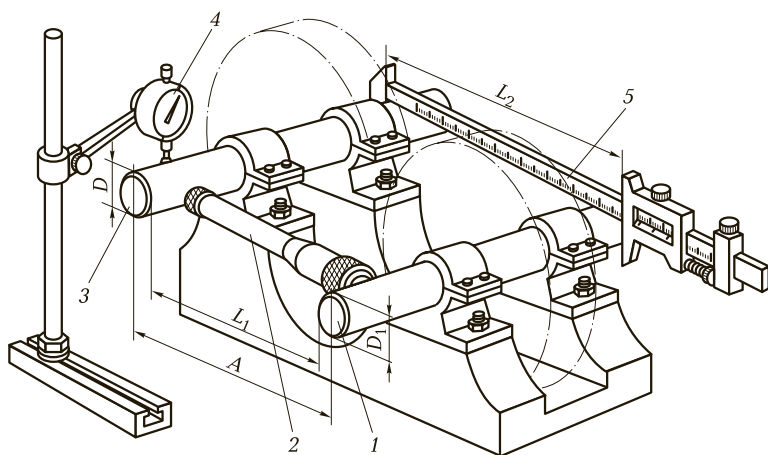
Схема контроля расстояния между осями валов цилиндрической зубчатой передачи:
